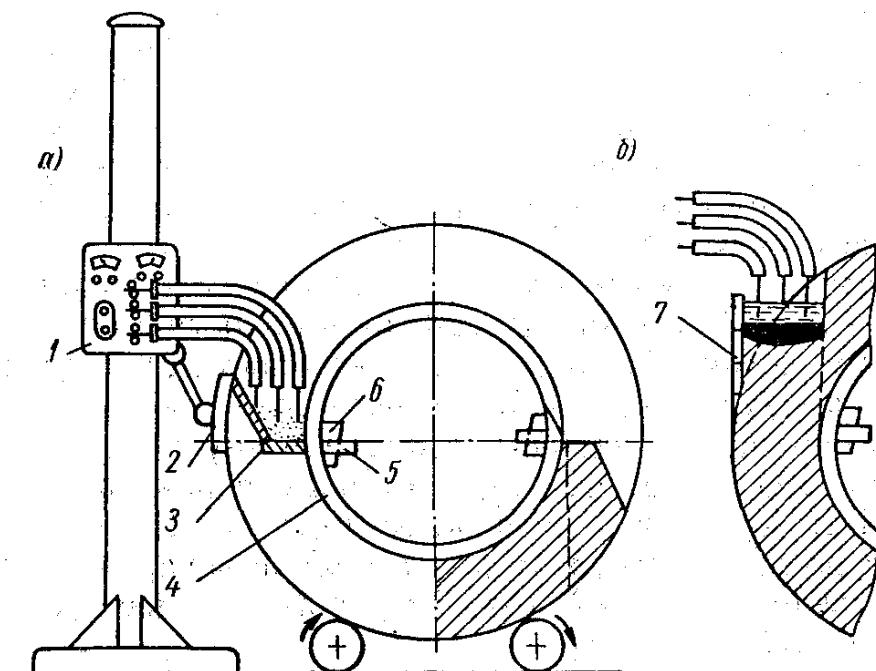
Электродуговая сварка кольцевых швов:
